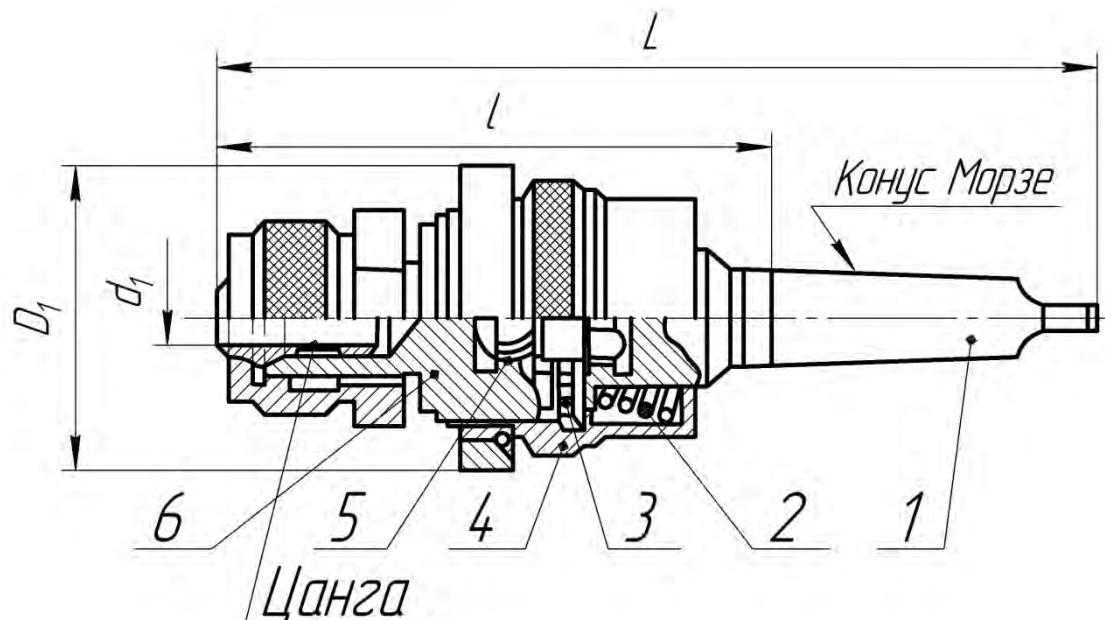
Качающийся и плавающий патрон для разверток
